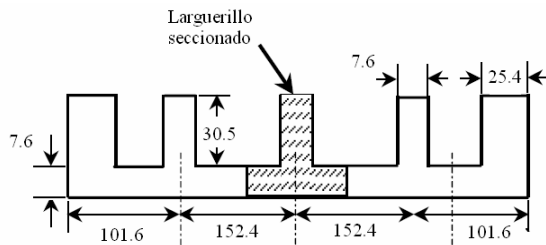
Corte transversal del panel, en el que se aprecia la localización de la grieta y el larguerillo seccionado [7].
